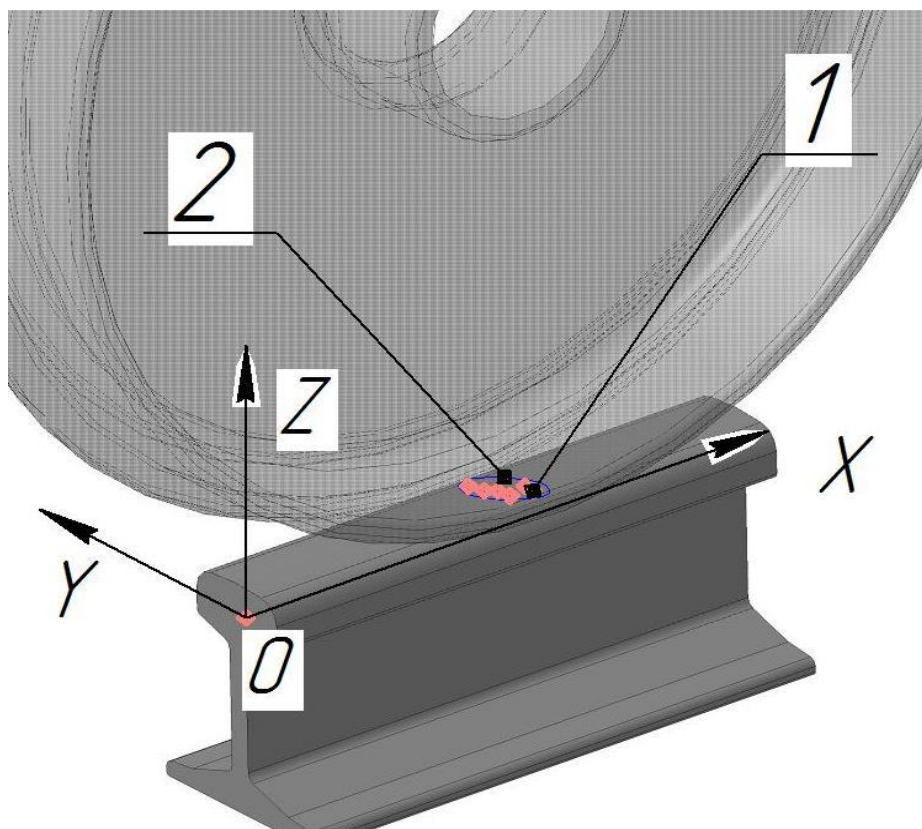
Опорна поверхня фрикційної пари колесо-рейка
